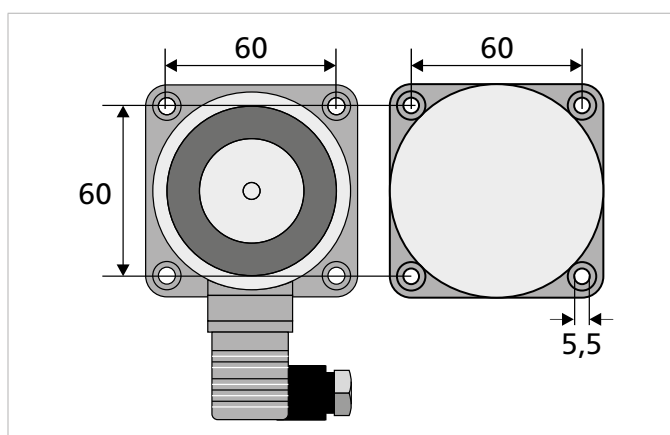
Abmessungen Montagelöcher (Angaben in mm)
